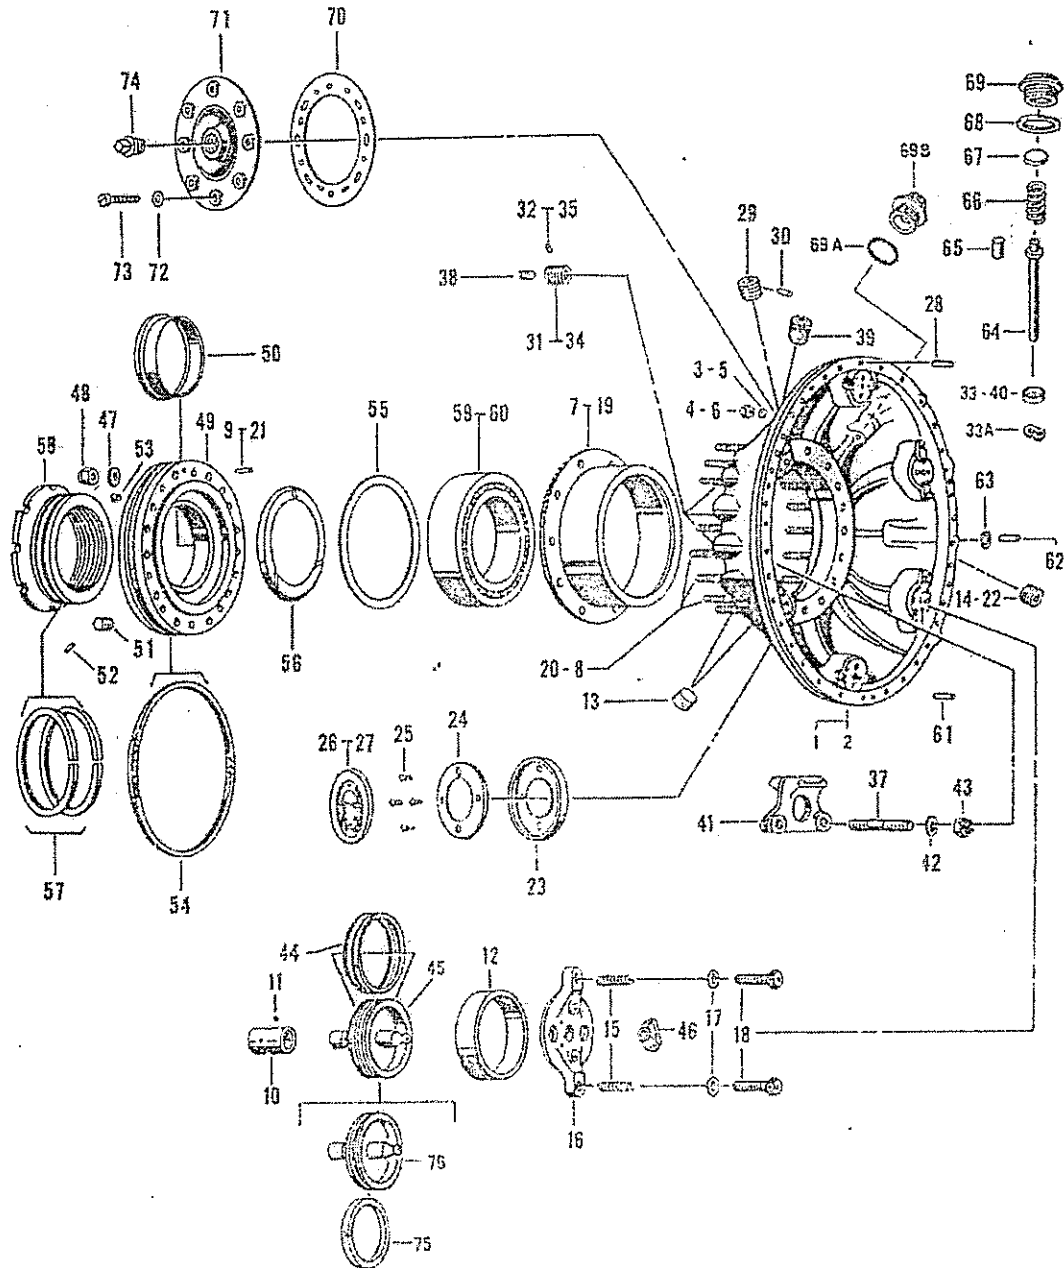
PLANETARY GEAR (19)
